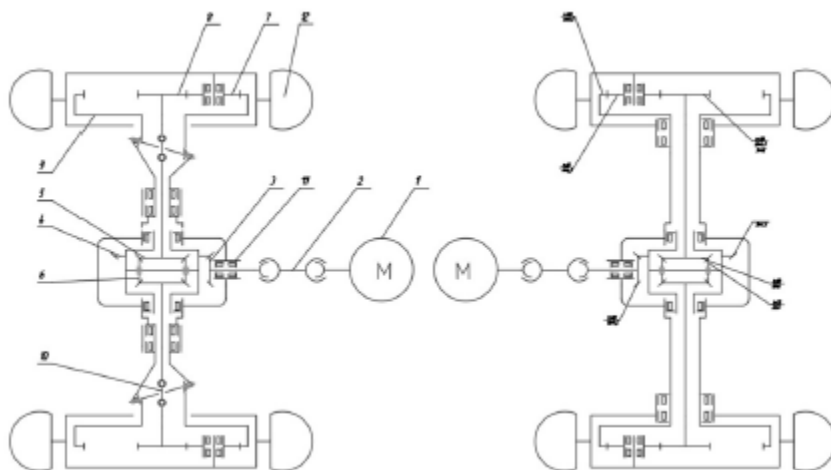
Кинематическая схема трансмиссии спортивного грузовика
